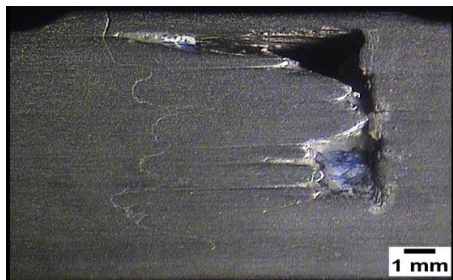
Hasil friction stir welding Aluminium 5052 dengan variasi feed rate
